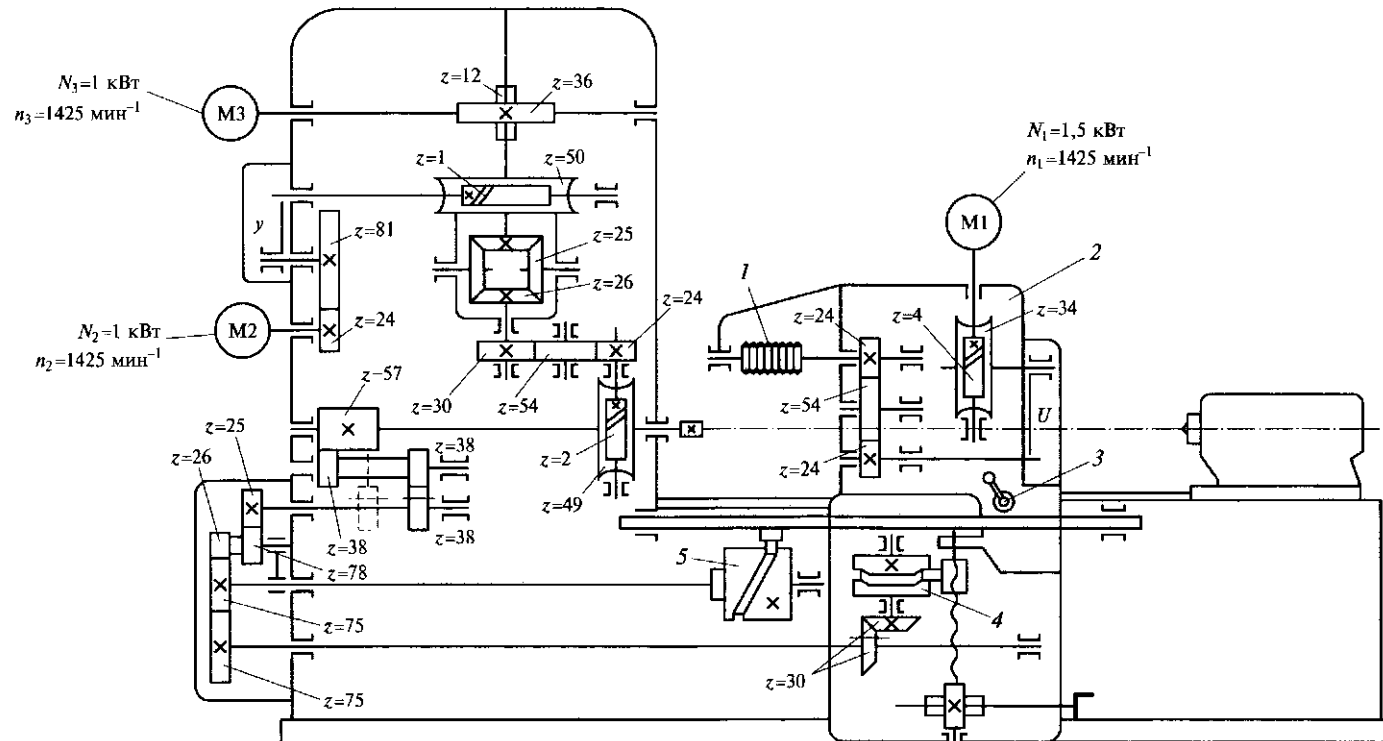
Кинематическая схема резьбофрезерного полуавтомата:
